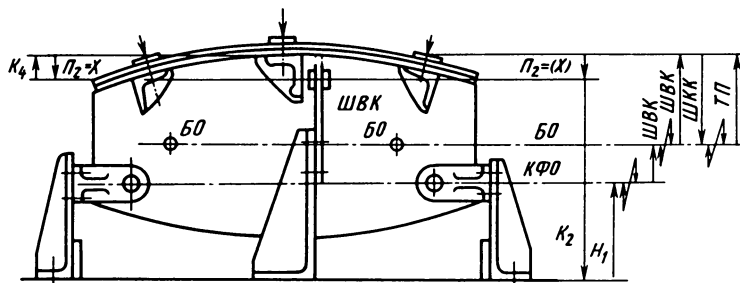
Схема переналаживаемого приспособления для образования сборочных отверстий (СО)
